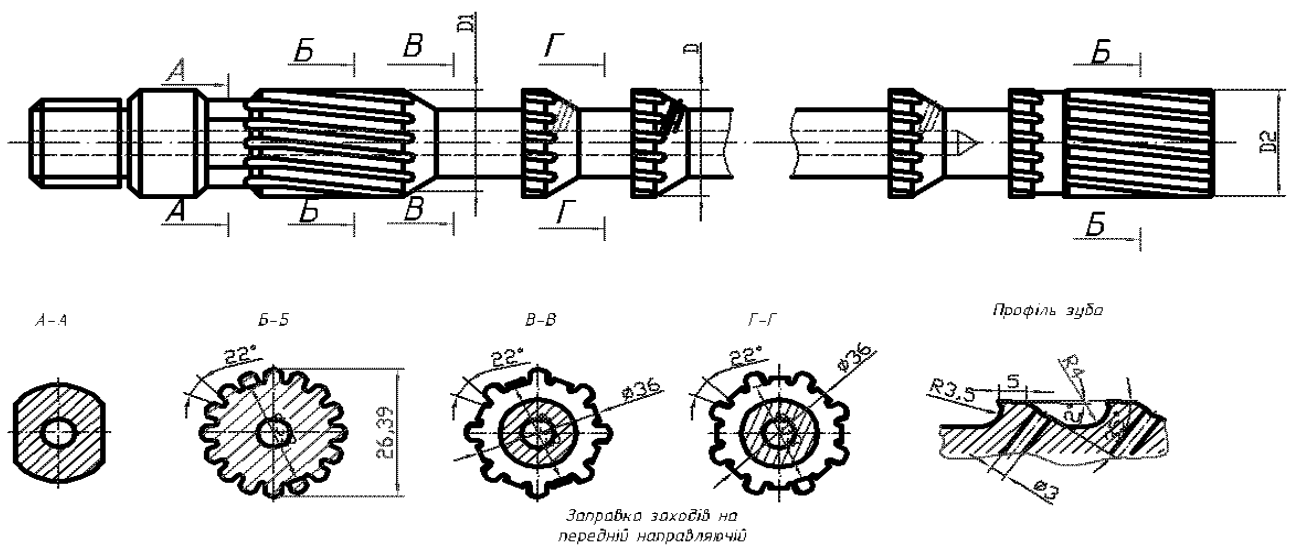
Протяжка з шахматно-шліцевою схемою різання для протягування гвинтових напівкруглих канавок
